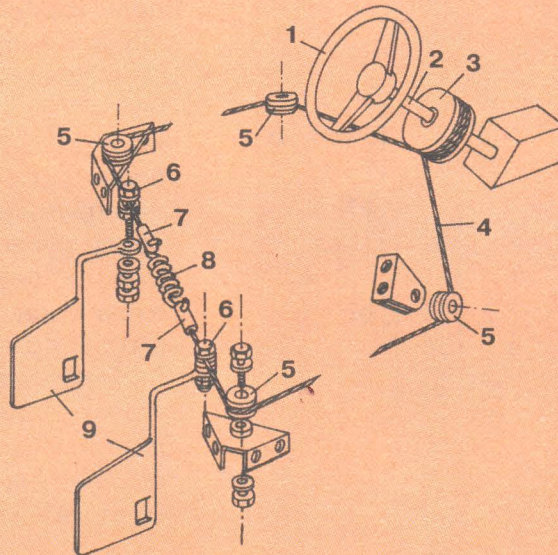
Кинематическая схема рулевого управления: 1 — рулевое колесо; 2 — рулевая колонка; 3 — рулевой шкив; 4 — трос; 5 — поворотный ролик; 6 — болт с поперечным отверстием; 7 — наконечник; 8 — пружина; 9 — рулевая лопасть.
